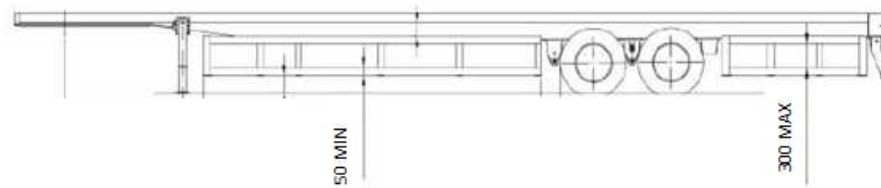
, Dimensiones de los largueros, Vista Lateral (dimensiones en mm)
